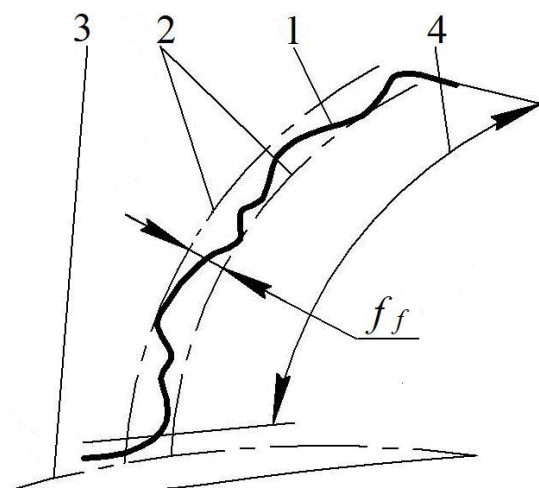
Погрешность профиля зуба: 1 – действительный торцовый активный профиль зуба; 2 - номинальные торцовые профили зуба; 3 – основная окружность; 4 - границы активного профиля зуба
